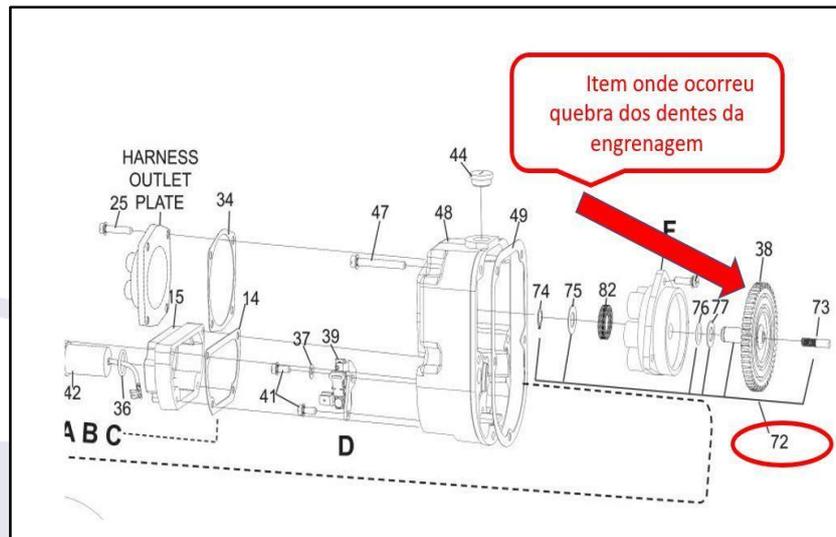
Visão esquemática das partes do magneto, com destaque para a engrenagem colapsada.
